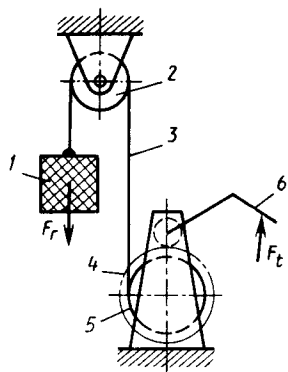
Схема подъемной лебедки: 1 — груз; 2 — отклоняющий неподвижный блок; 3 — гибкий элемент (канат); 4 — зубчатая передача; 5 — барабан; 6 — рукоятка
